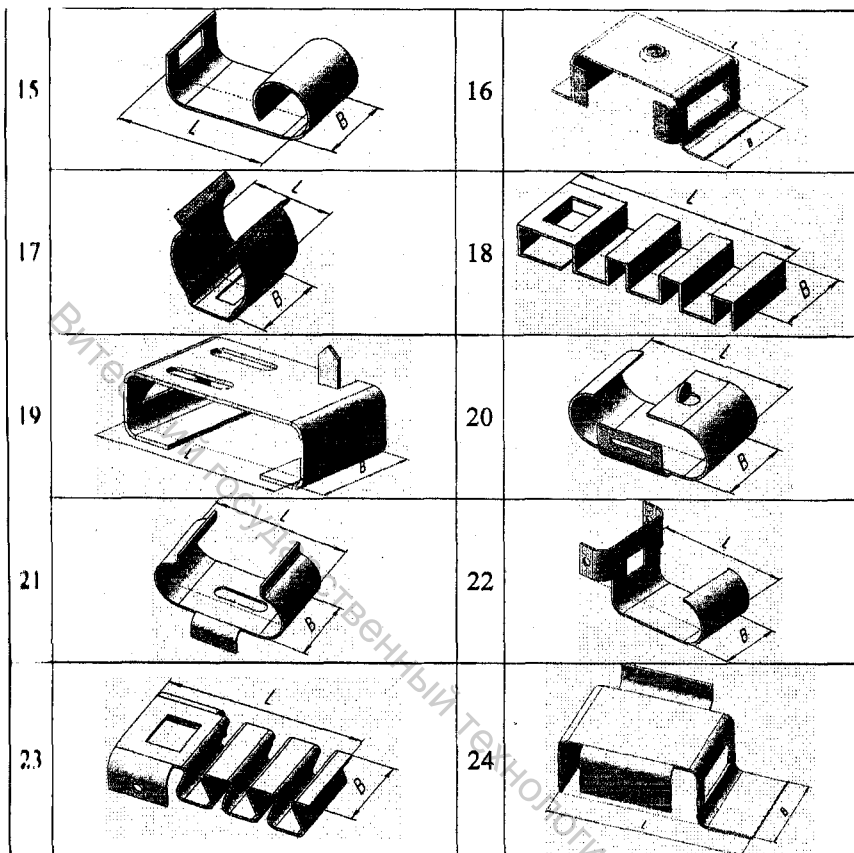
Схемы простановки координат отверстий в изогнутых заготовках
